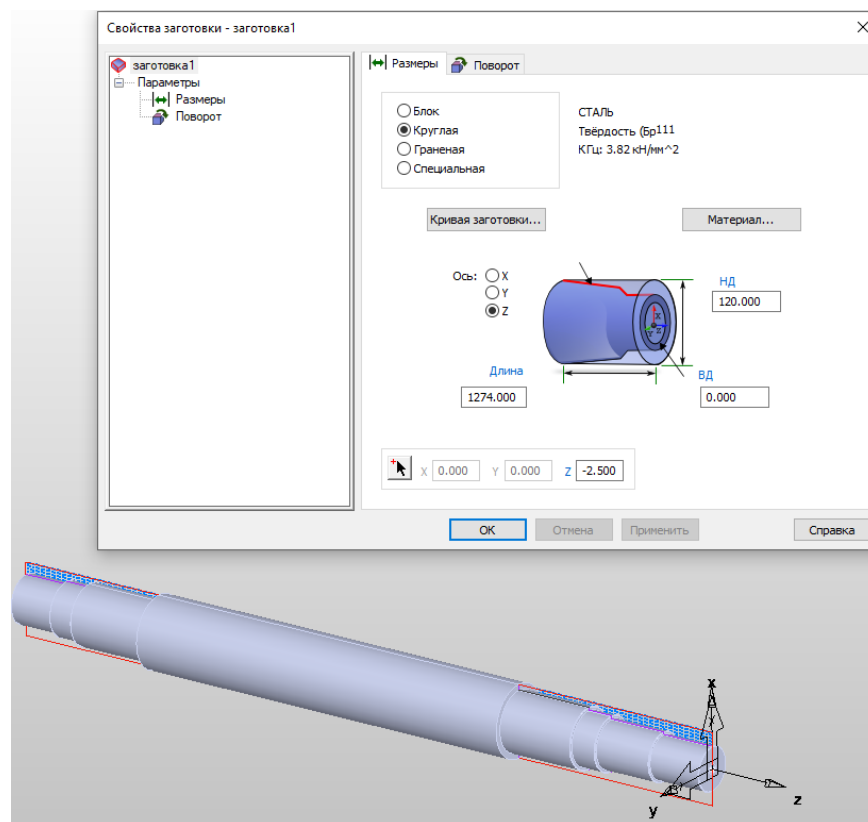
Загальний вигляд імпортування деталі та обраних параметрів заготовки
